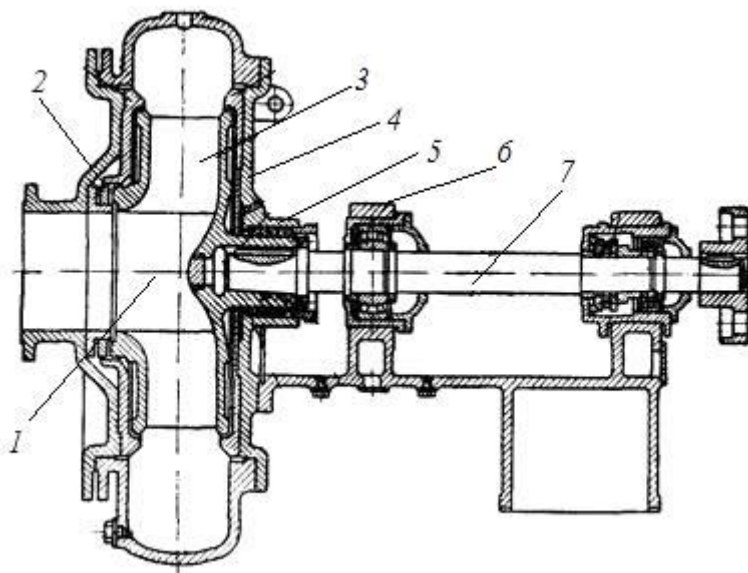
Схема устройства грунтового насоса ЗГМ-350А: 1 – рабочее колесо; 2 – передняя половина корпуса; 3 – футеровка; 4 – задняя половина корпуса; 5 – сальниковый узел; 6 – опорная стойка; 7 – вал
